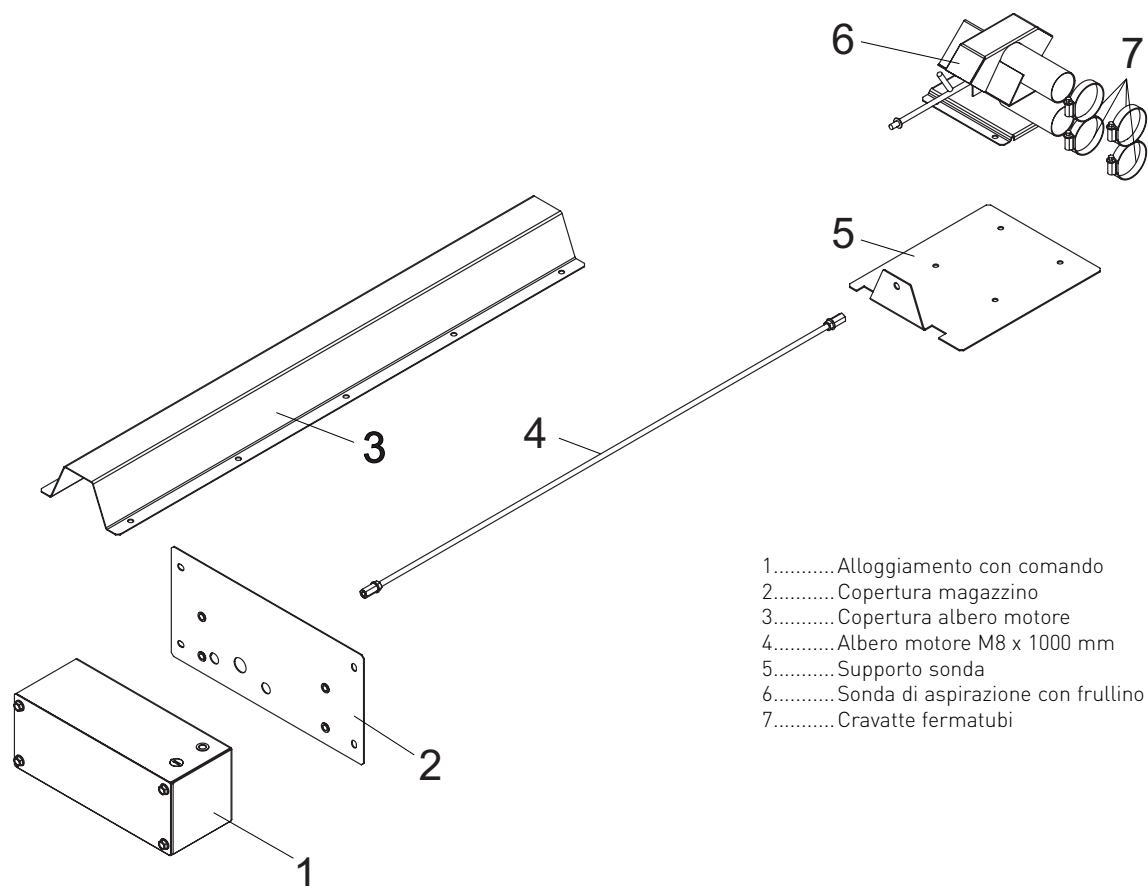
Singoli pezzi del serbatoio in lamiera d'acciaio – vista dall'alto
